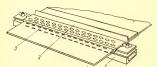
Приспособление для стыковки конвейерных лент с помощью П-образных скоб: 1- нижияя плита; 2- верхияя траверса; 3- распределитель скоб
